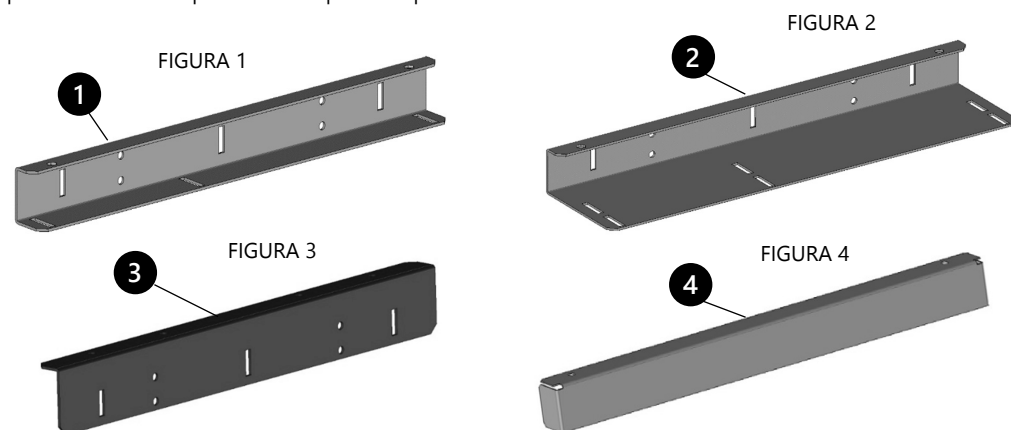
Perfil cantonera para fijación dentro de la estructura (perfil menor);
